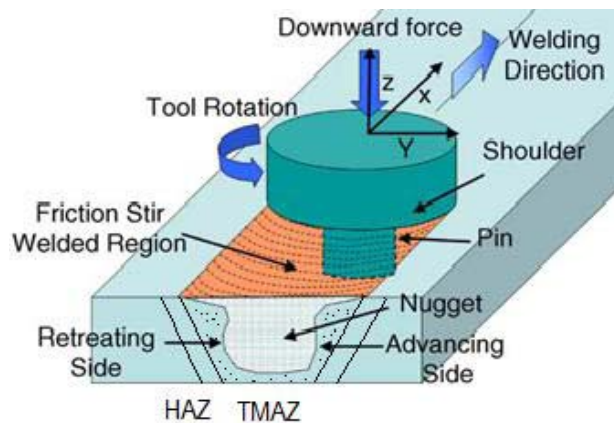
Procédé de soudage FSW d'un joint bout à bout [Mishra 2005].
